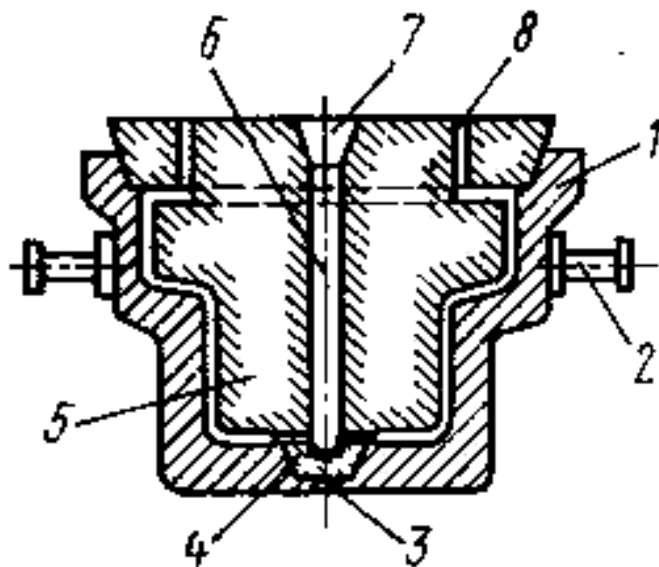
Конструкція нероз'ємного коклія для алюмінієвого виливка:
